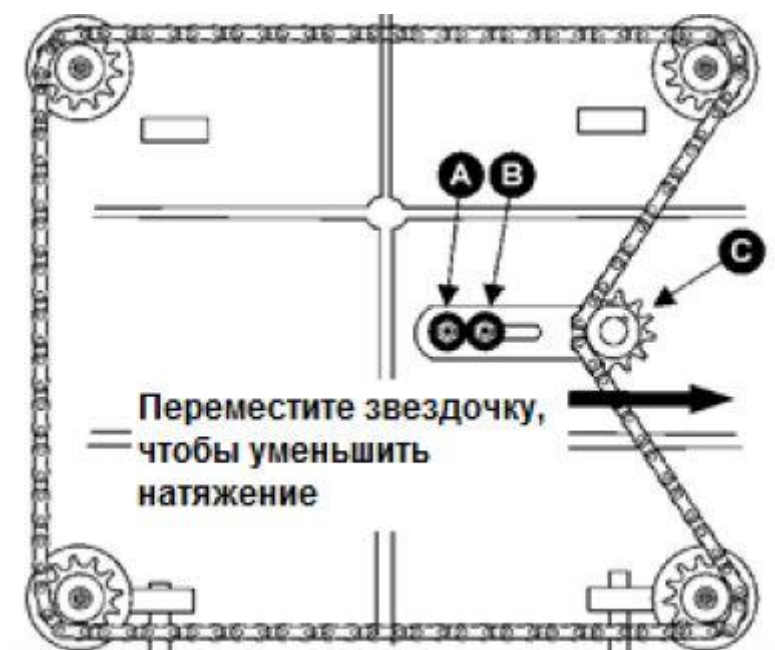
Регулировка параллельности рабочего стола к фрезерной головке
